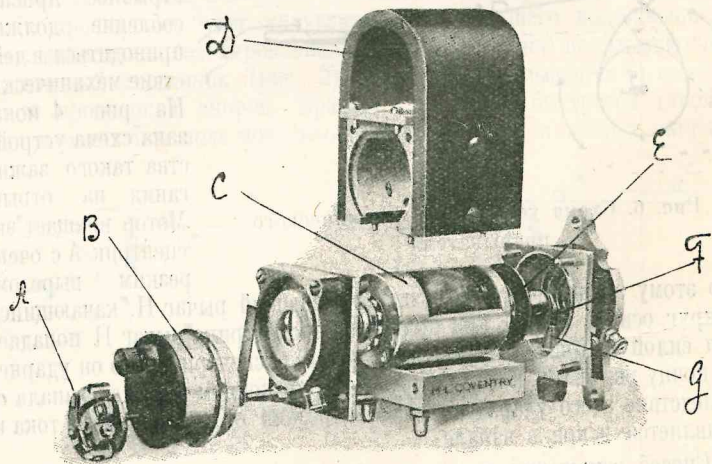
Части разобранного магнето: А — прерыватель, В — коробка прерывателя, С — якорь с обмоткой, Е — коллектор на якорь, Г — уголек, г — угледержатель, Д — подковообразные магниты.
